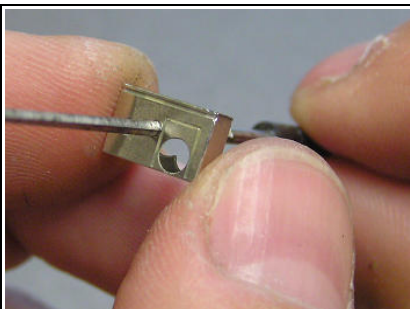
Mittleres Loch im Getriebekasten auf 1,4mm (entspricht Buchsenaußendurchmesser H1014) aufreiben
